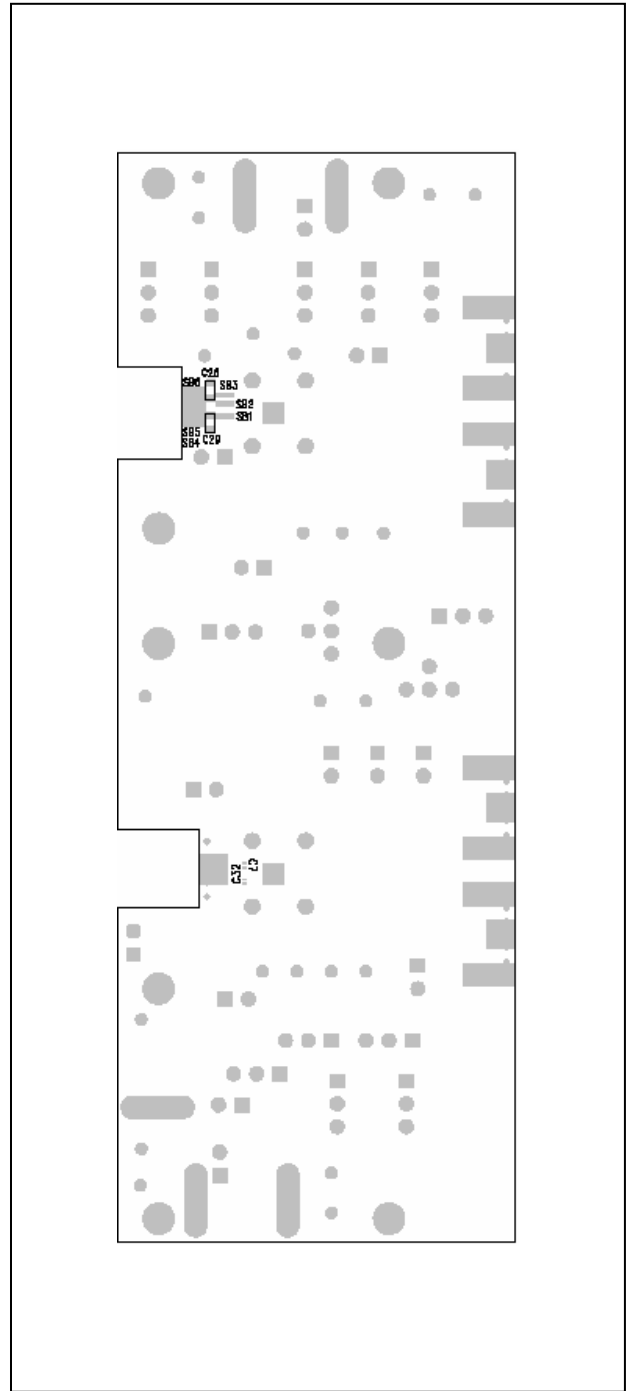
MAX3738 评估板 PCB 布局 — 焊接层
